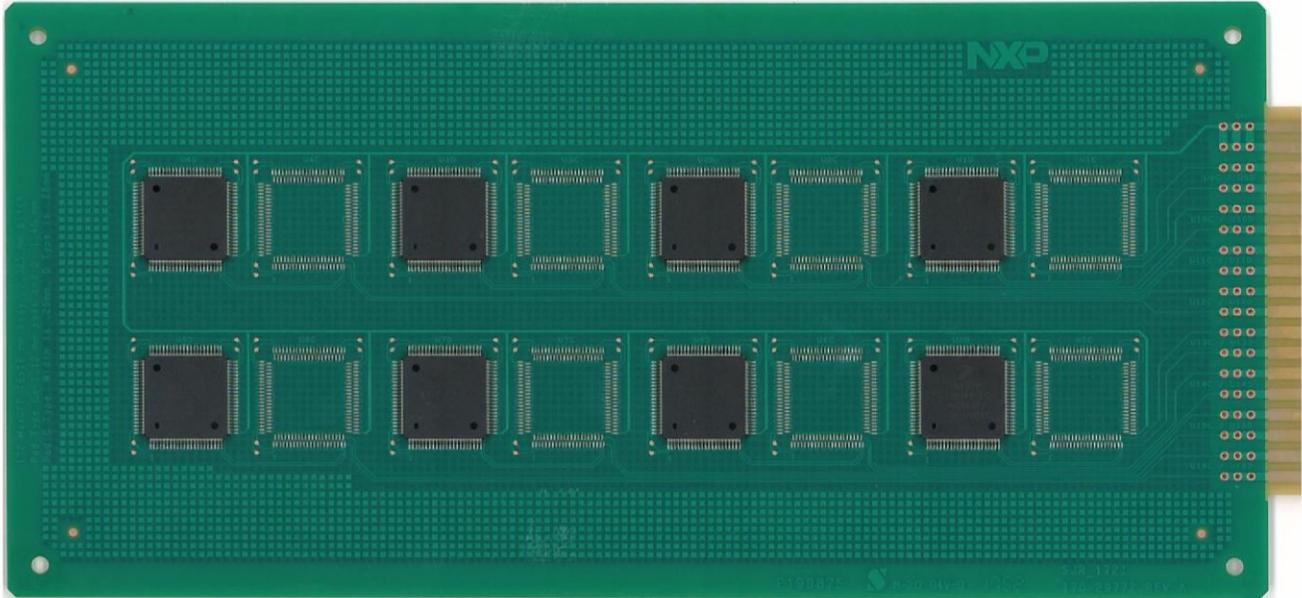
ボードレベル信頼性テスト用 172HDQFP PCB
